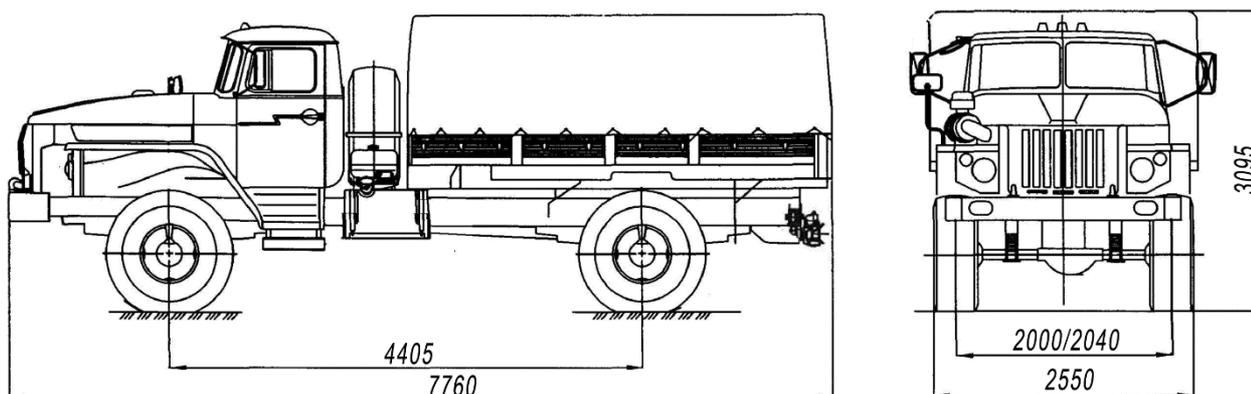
Основные размеры автомобиля Урал-43206-0111-41
